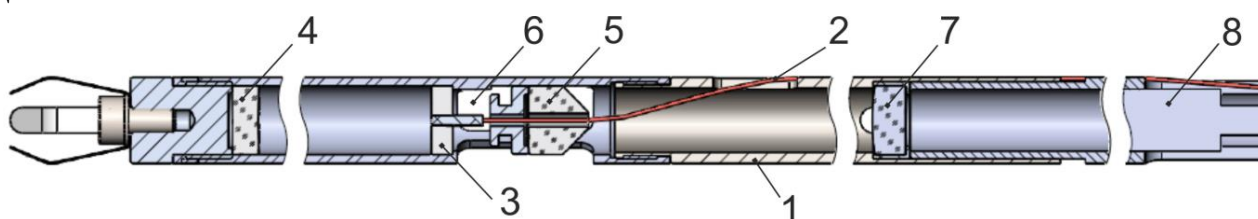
Конструкция зонда: 1 – корпус; 2 – оптоволоконно; 3 – ДОЭ; 4 – сферическое зеркало; 5 – коническое зеркало; 6 – окна в корпусе зонда; 7 – линза; 8 – эндоскоп
